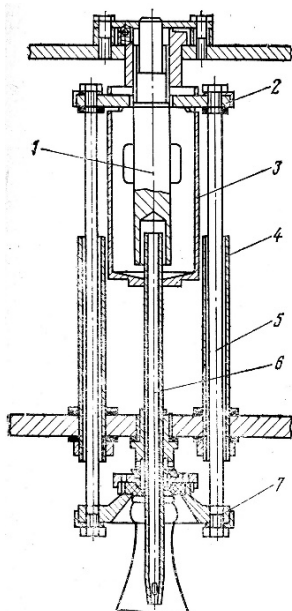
Дозуючий пристрій розливочно-закупорювальної машини марки Б7-ВДР-1.5.
